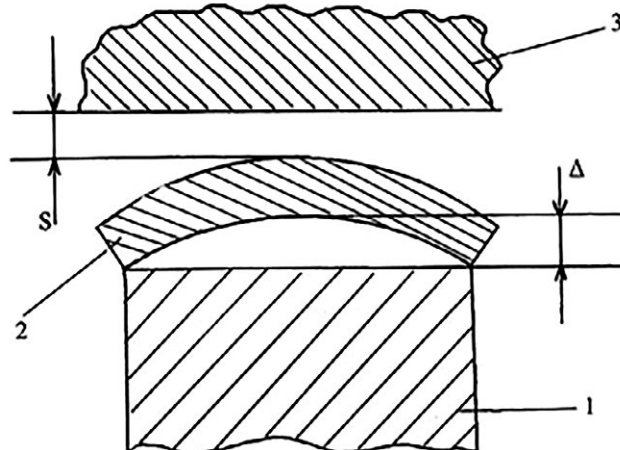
Схема поперечной деформации вкладыша 2 с образованием прогиба Δ : 1 — шатун; 2 — вкладыш; 3 — шейка вала; S — зазор в подшипнике.
